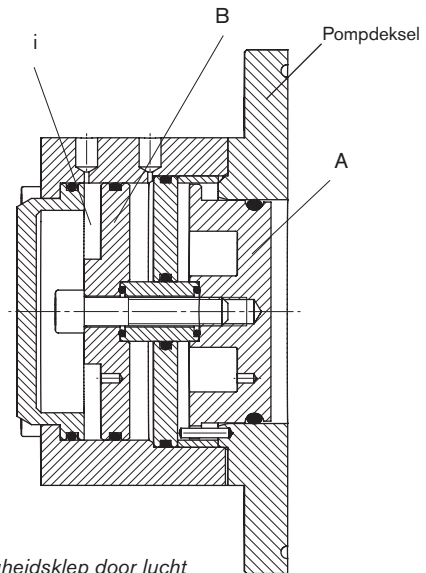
Veiligheidsklep door lucht belast – met lucht geopend gedeeltelijk open
